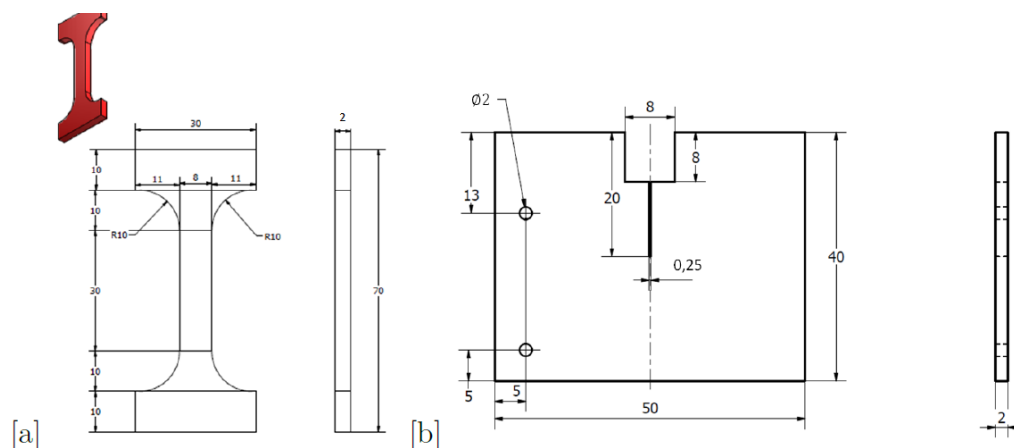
Géométries des échantillons (a) éprouvette de traction (b) éprouvette de type tension compacte.
